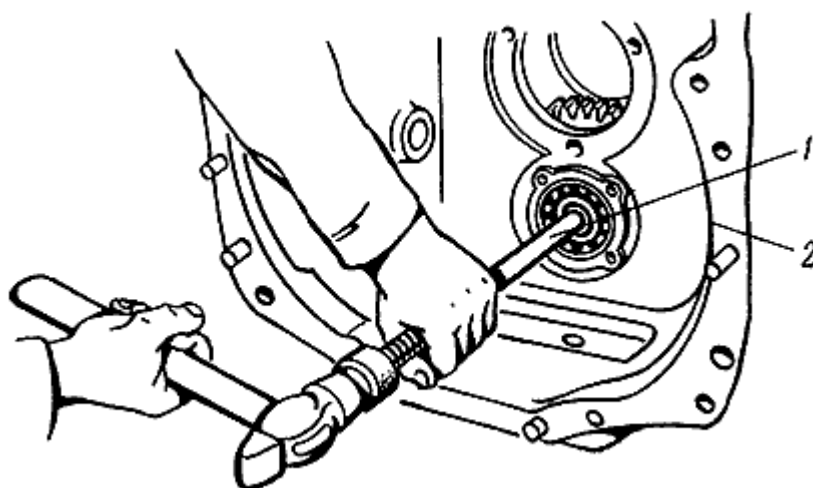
Выпрессовка ведомого вала привода ВОМ, снятие шестерен I и II ступеней, снятие соединительной муфты:
